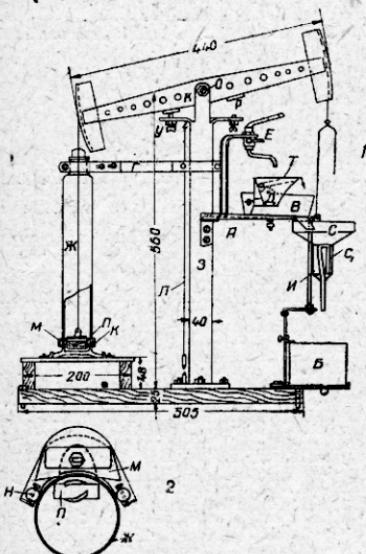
Схематический чертеж автоматической магнитной мешалки:
